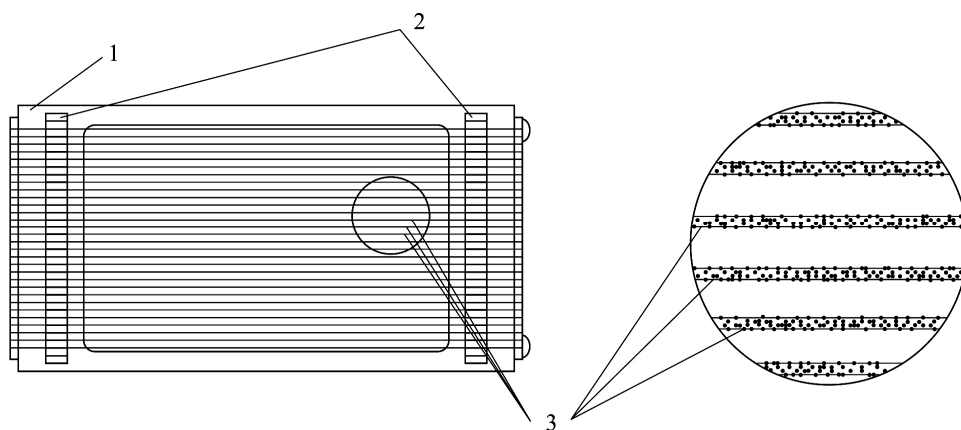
Инструмент для резки струнами с закрепленными алмазными зёрнами.
